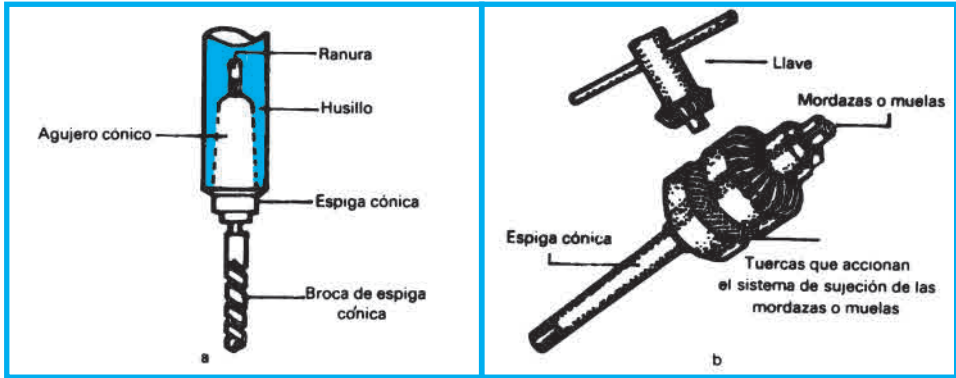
Forma de colocar la broca en la taladradora: a) en el husillo de la taladradora; b) en el portabroca o mandril.
